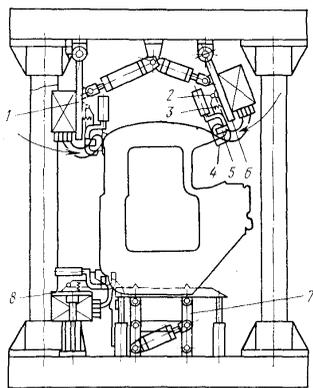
Схема сварки кабины на многоэлектродной машине
